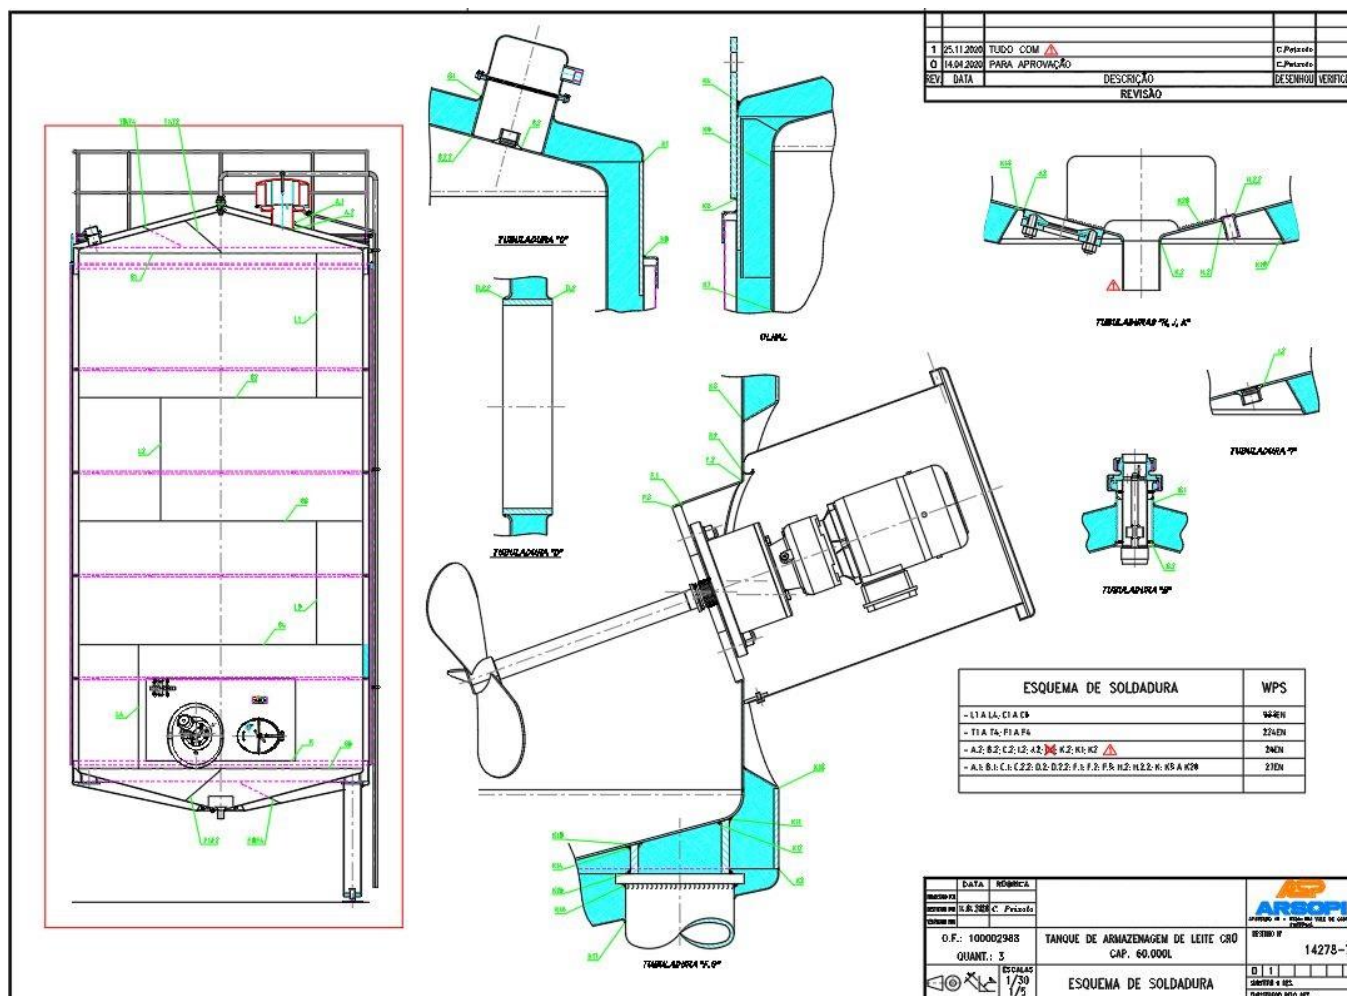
Desenho de fabrico de tanque de armazenagem.
